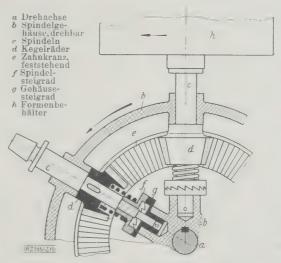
Spindelgehäuse der Hohlformmaschine.
